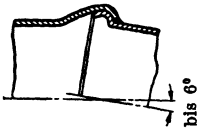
Klöpperkugelschweißmuffe.
